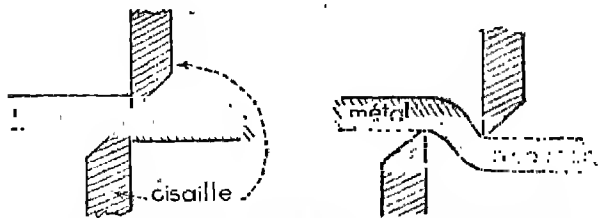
Les lames d'une cisaille doivent glisser l'une sur l'autre sans jeu (à gauche) ; sinon la feuille plie et n'est pas tranchée (à droite).
